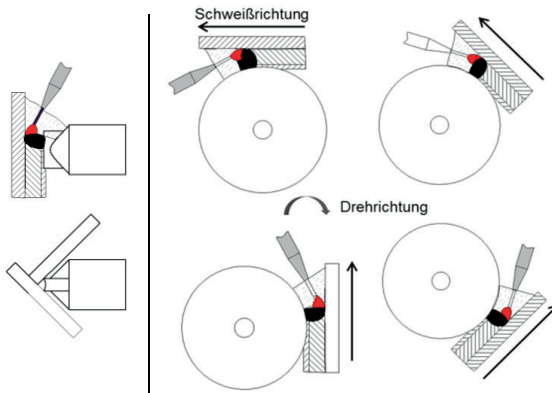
Varianten zum UP-Zwangslagenschweißen, links: Formgleitstück; rechts: Formscheibe
